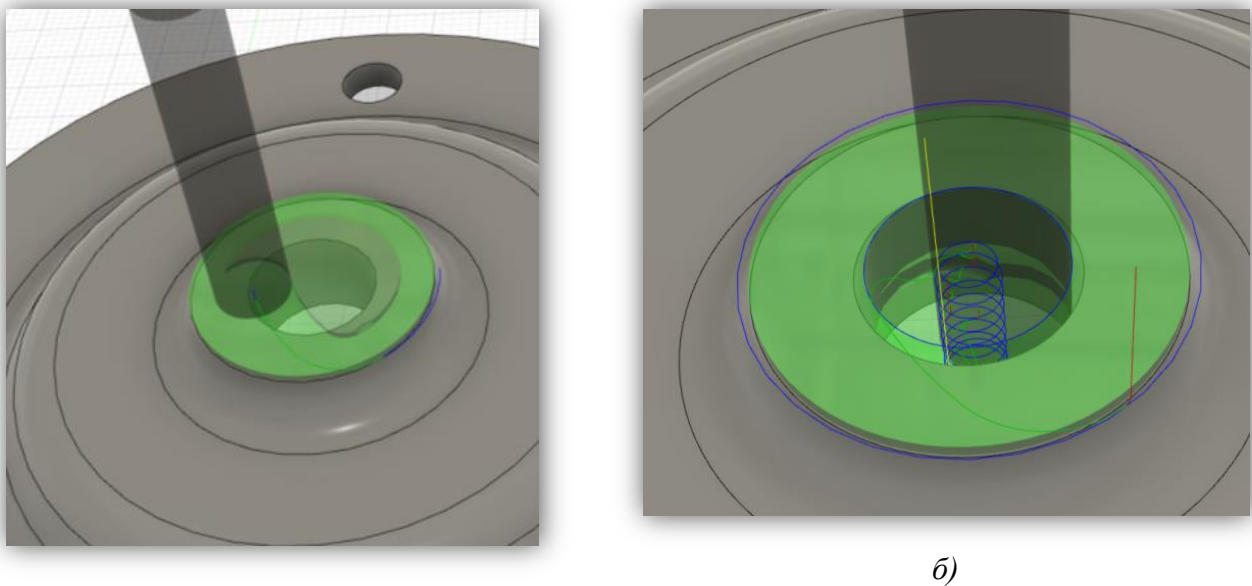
Симуляція у програмному середовищі Fusion 360 фрезерної з ЧПК технологічної операції: а) фрезерування торця; б) фрезерування отвору методом гвинтової інтерполяції.
